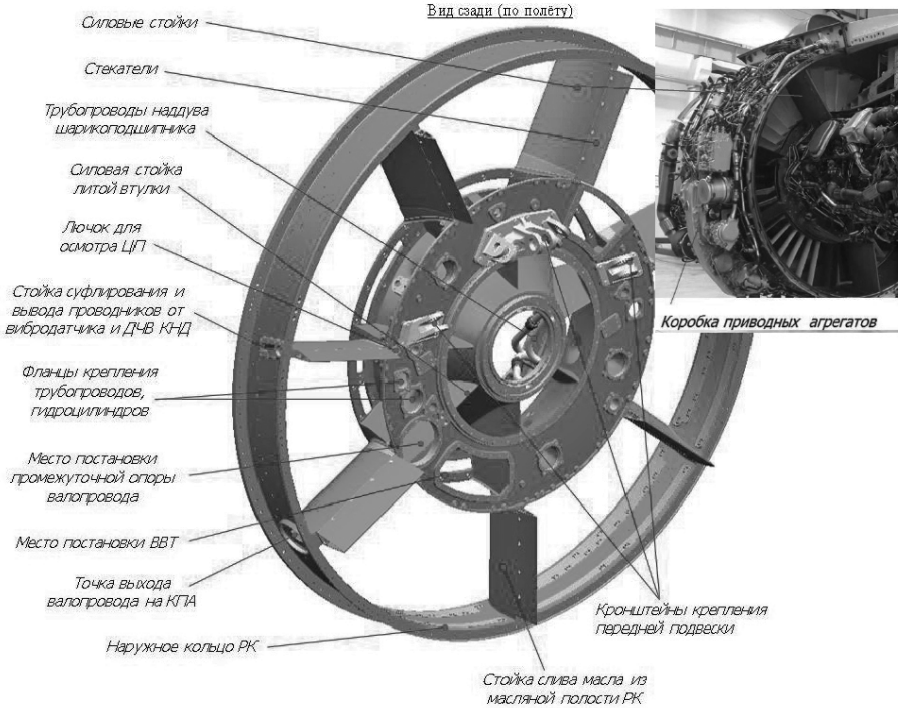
Корпус разделительный и коробка приводных агрегатов
